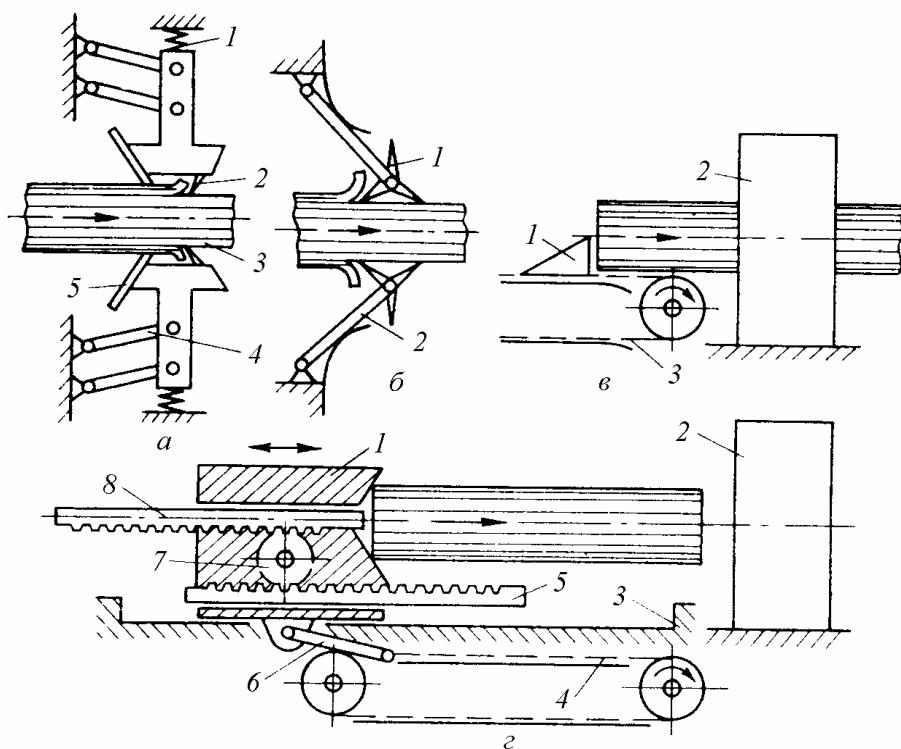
Продольные ножевые окорочные станки: а – режущий механизм с плоскими ножами; б – режущий механизм со звездчатыми ножами; в – подающий механизм с упором; г – подающий механизм с толкателем
